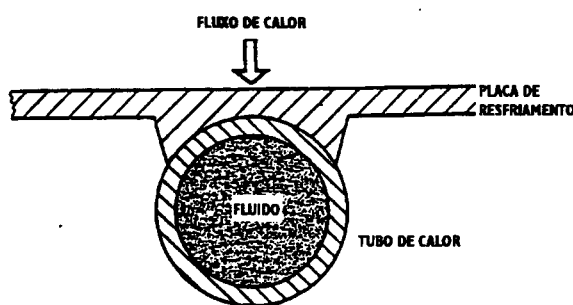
Tubo de calor soldado a uma placa de resfriamento.
